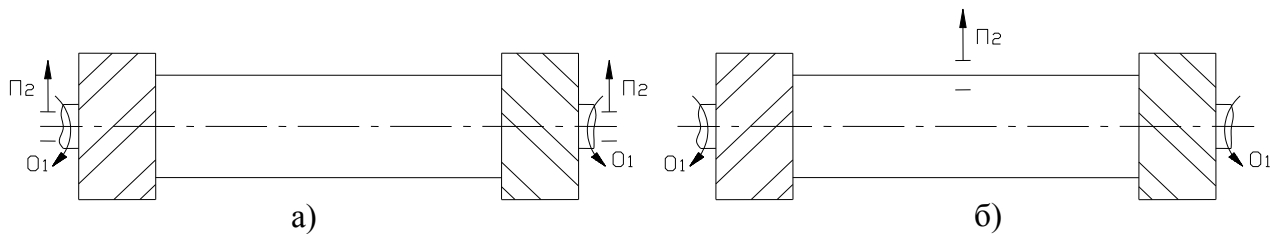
Схема обробки торців торцевими фрезами з рухомою (б) і нерухомою (а) заготовкою
